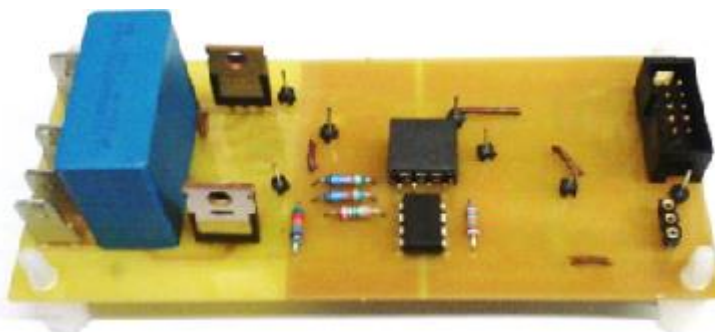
Vista superior da segunda versão do PCB desenvolvido.
